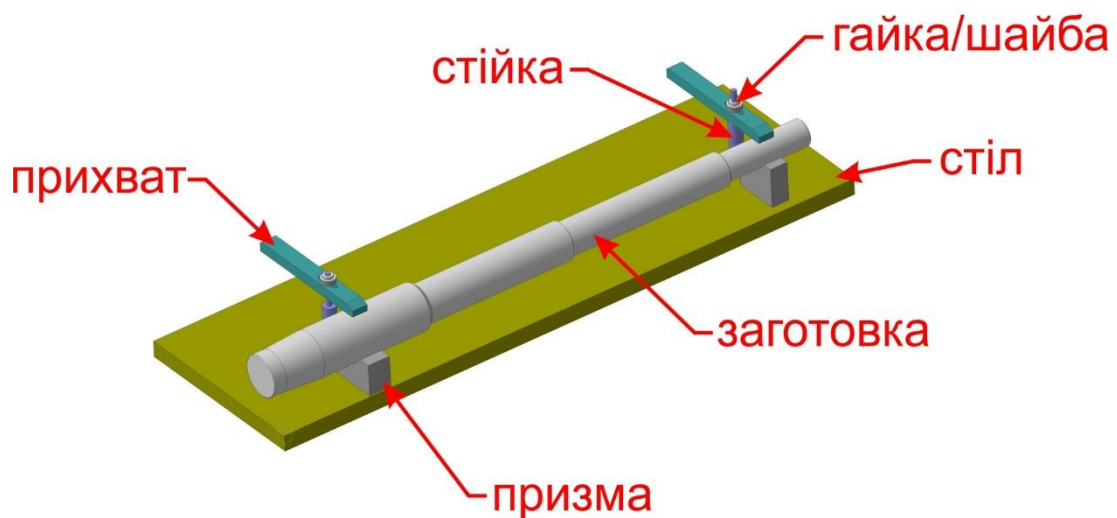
Твердотільна модель системи «пристрій-заготовка»
